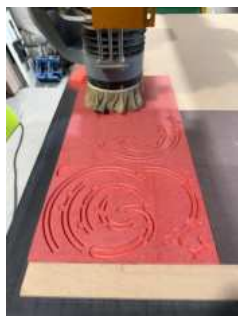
Detail slepení a kulatých frézovaných cest ve hře Balance (Zdroj: archiv autorky)
